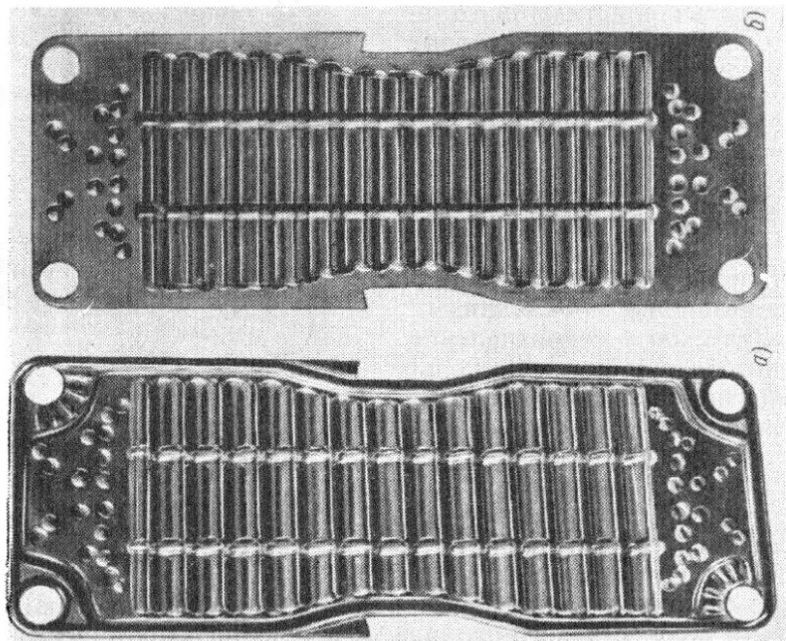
Ленточно-поточные пластины «Альборн-Прогресс» с крупными горизонтальными гофрами синусоидального профиля: а — печатная пластина с двусторонними прокладками; б — четная пластина с плоскими кромками
